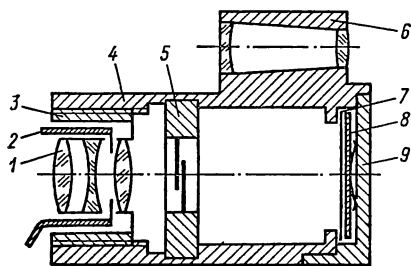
Схема фотоаппарата «Смена»: 1 — объектив-триплет; 2 — шкала ирисовой диафрагмы; 3 — фокусирующая оправа, 4 — корпус; 5 — центральный затвор; 6 — телескопический видоискатель; 7 — фотопленка; 8 — планка, прижимающая фотопленку; 9 — задняя крышка
